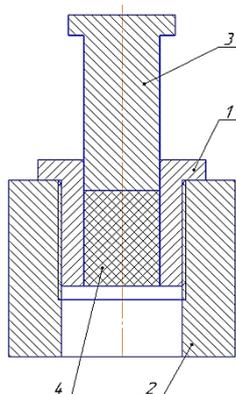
Приспособление в сборе (1 – матрица; 2 – обойма; 3 – шток (пуансон); 4 – опытный композит)
